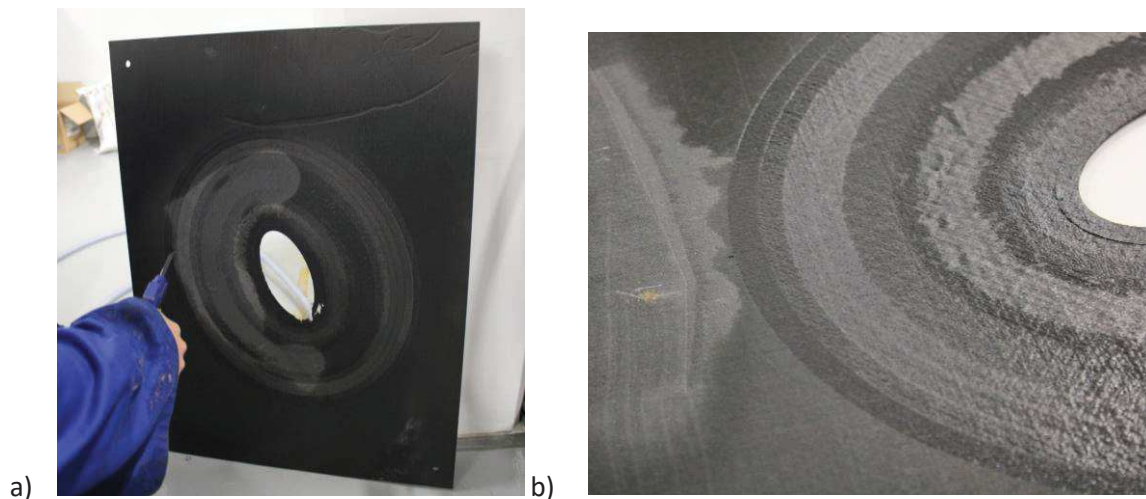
a) Séchage de la plaque composite et b) apparition visuelle des défauts de fabrication
